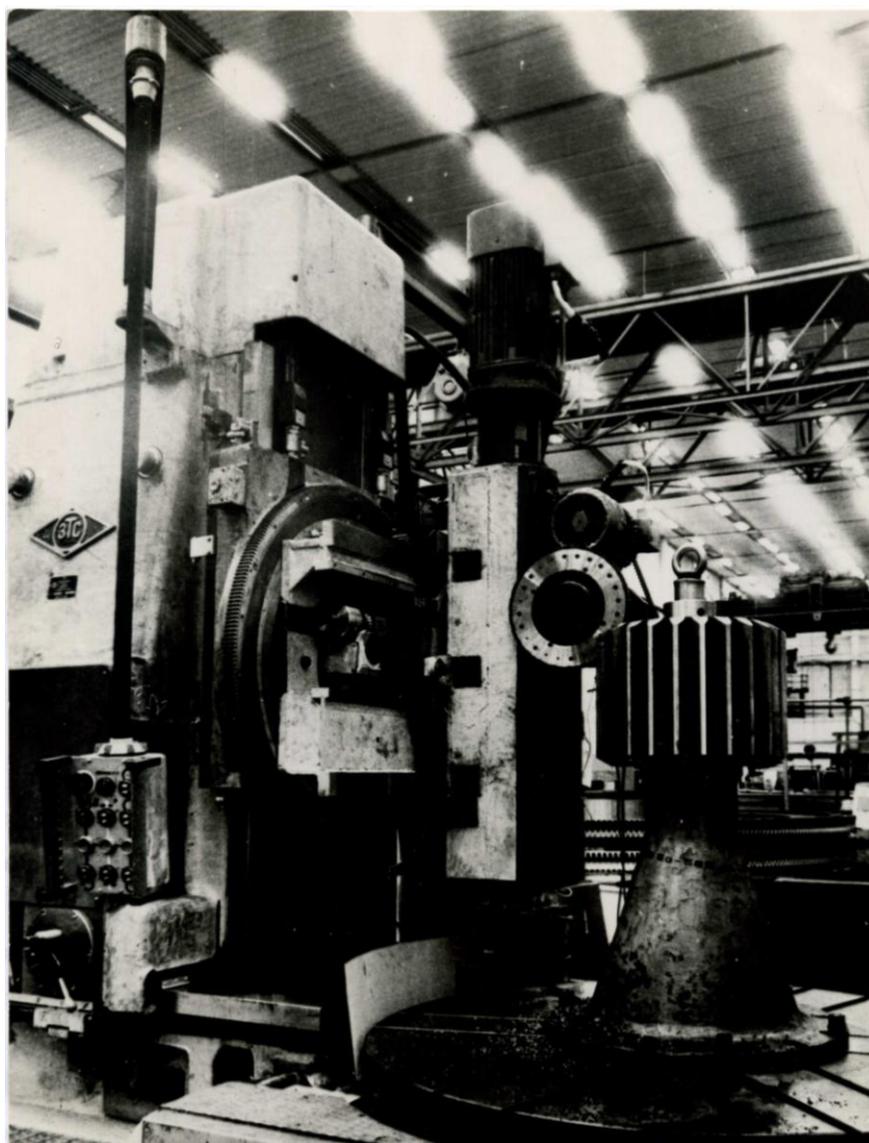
Обработка закаленного колеса $m = 20$ мм, $z = 29$ с использованием специального суппорта для вертикально-зубофрезерного станка мод. 5A342П
